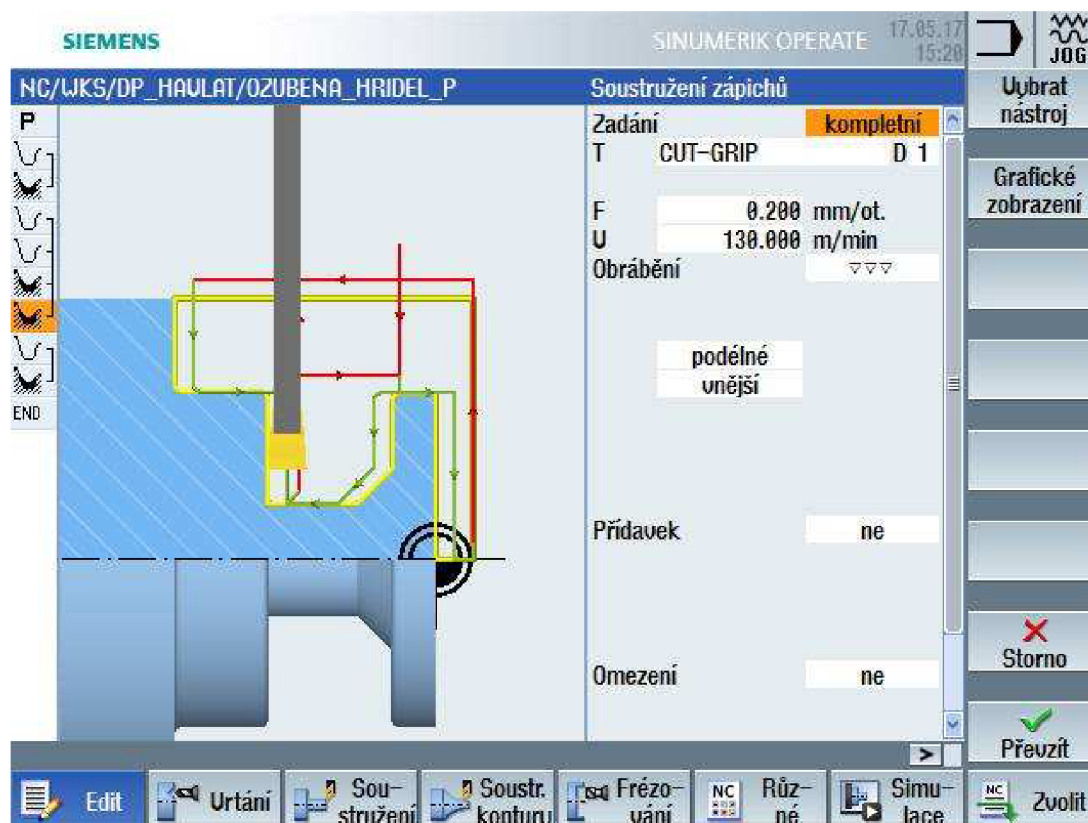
Kontura definující hranici obráběného objemu materiálu
